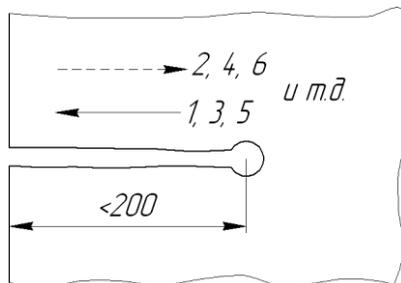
Форма разделки под сварку сквозной трещины
